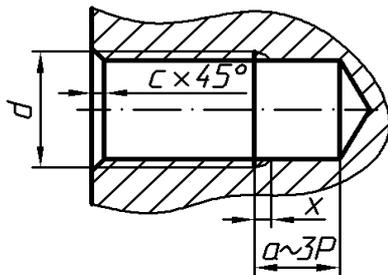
Внутренняя резьба в глухом отверстии:
